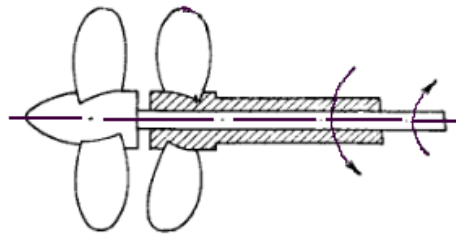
Схема рушійного пристрою АНПА з співвісними гребними гвинтами протилежного обернення
